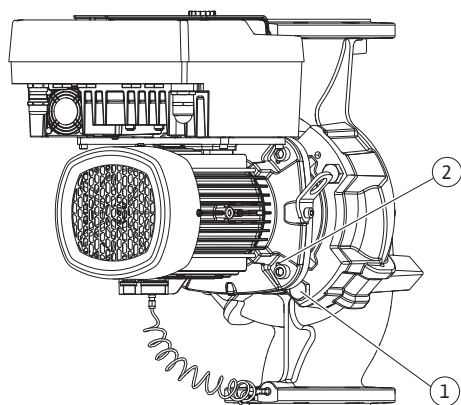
Abdrücken des Einstecksatzes über Gewindebohrungen (je nach Pumpentyp)
